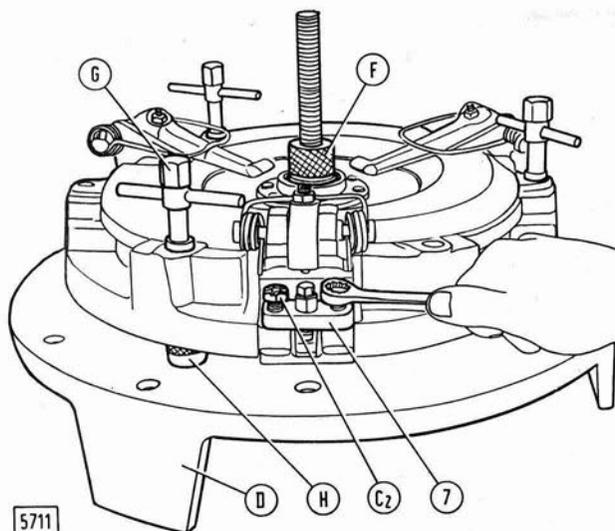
Démontage (et montage) de l'embrayage 10" sur le plateau universel A 711063/68 B (D).
